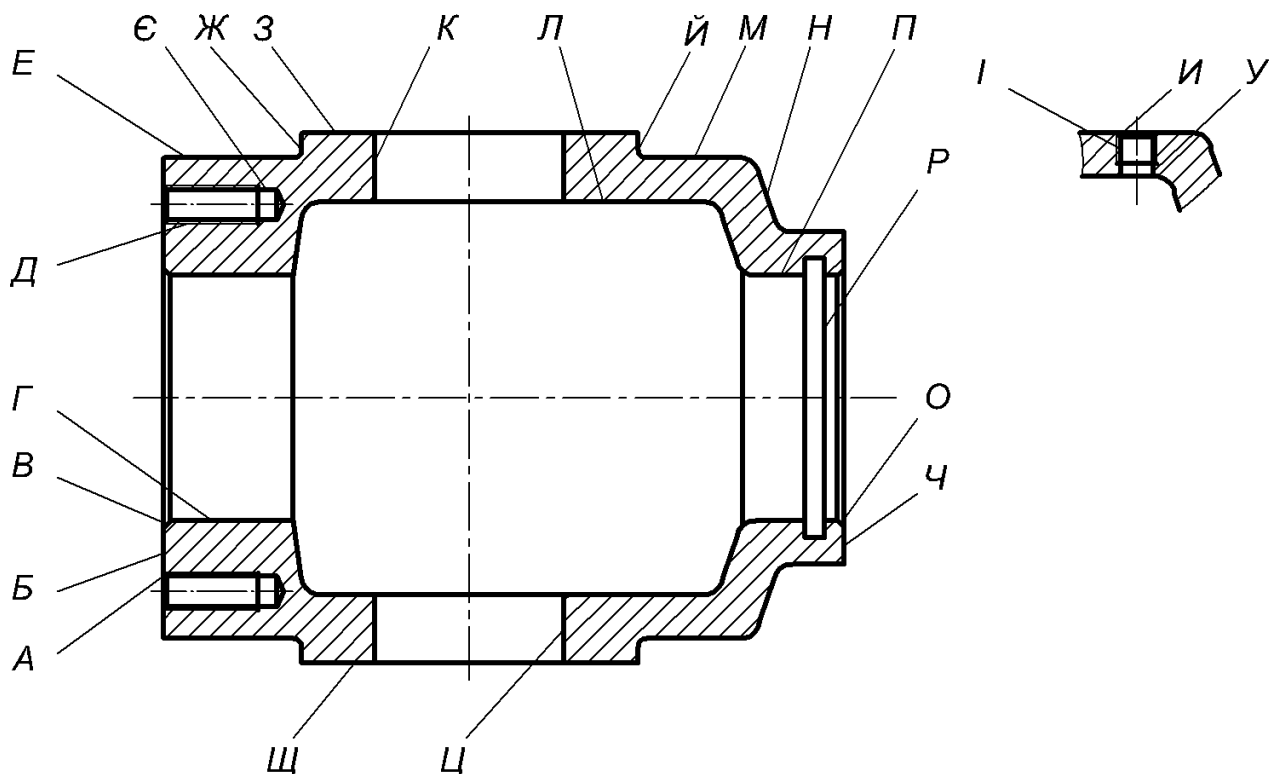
Позначання всіх поверхонь корпуса
